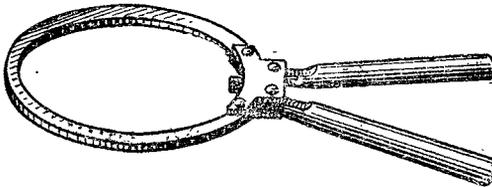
Приспособление для снятия и установки поршневых колец на поршень двигателя
